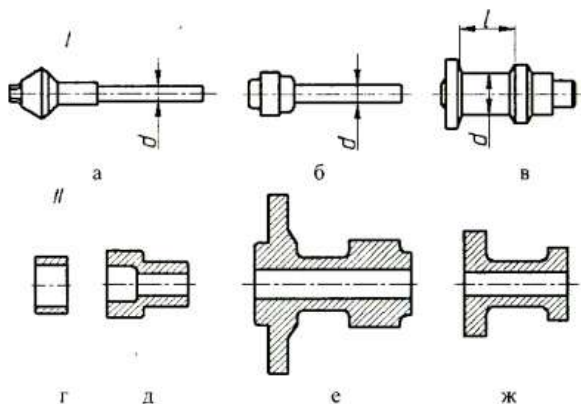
Номенклатура заготовок зубчастих коліс, які штампуються на горизонтально кувальних машинах: I група: а – конічне зубчасте колесо-вал, б – циліндричне зубчасте колесо-вал, в – двухвінцеве зубчасте колесо; II група: г – вінець, д – зубчасте колесо з маточиною і отвором, е – зубчасте колесо з фланцем і отвором, ж – двухвінцеве зубчасте колесо з отвором
